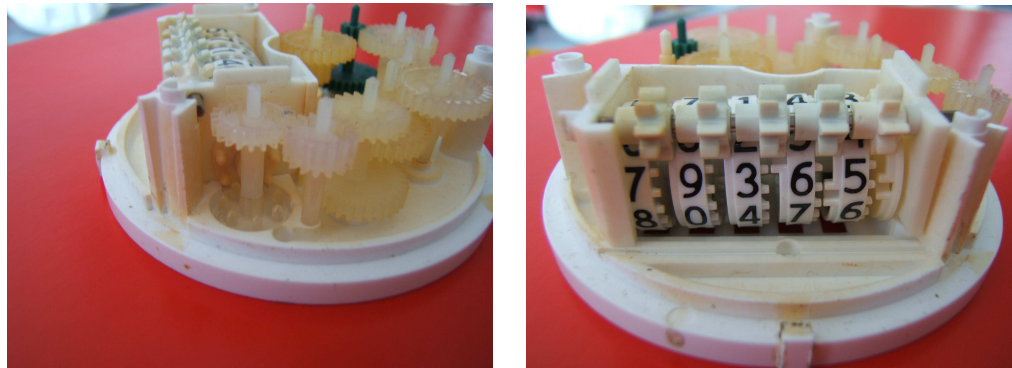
Mecanism cu angrenaj cu bolțuri
